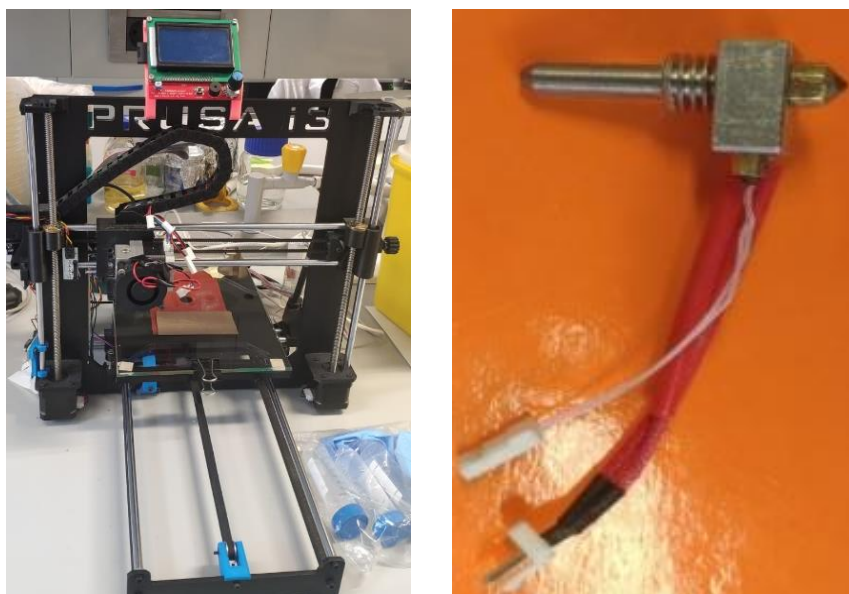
Izquierda: Impresora 3D de los laboratorios del CIBA, en ella se imprimen los parches. Derecha: boquilla extrusora con termistor y cartucho calefactor.
